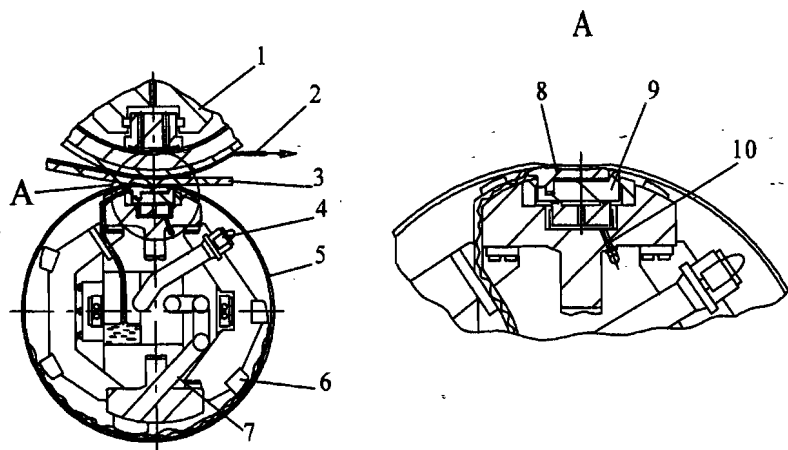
Поперечное сечение вала башмачного типа с гибкой оболочкой: 1 – вал с регулируемым прогибом; 2 – сукно; 3 – бумажное полотно; 4 – распределитель масла; 5 – гибкая оболочка; 6 – направляющие планки рубашки; 7 – обратный слив; 8 – башмак; 9 – прижимной элемент 10 – подача масла под давлением
